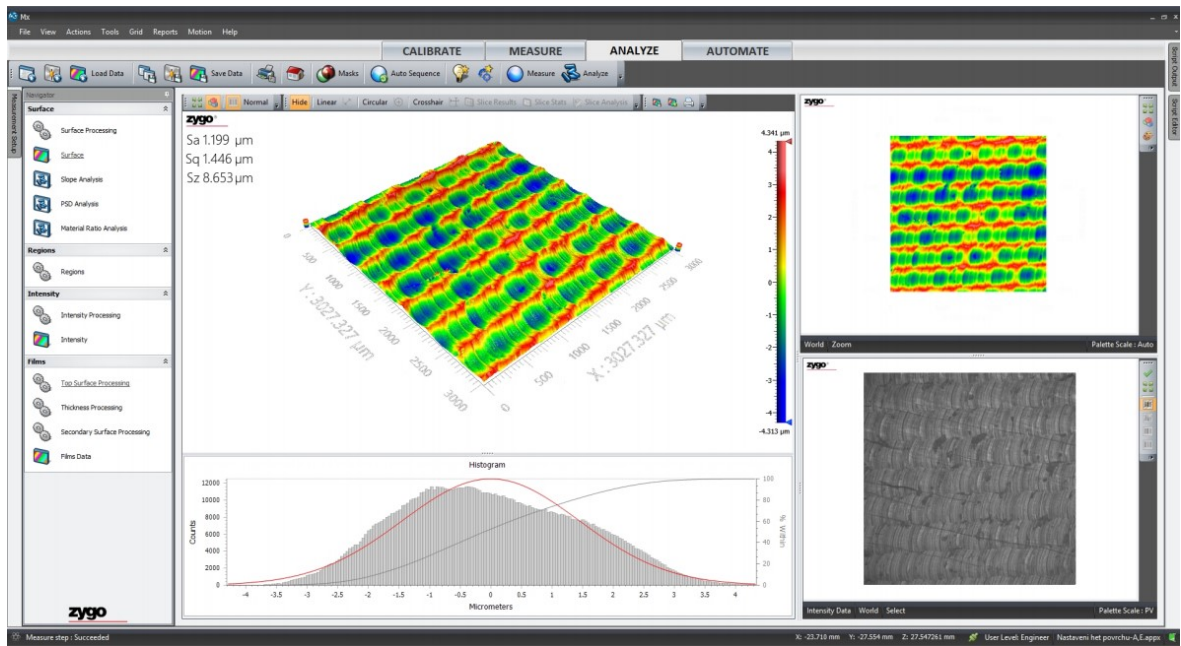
Obrobek z materiálu 1.0570, naměřená oblast: 1A
